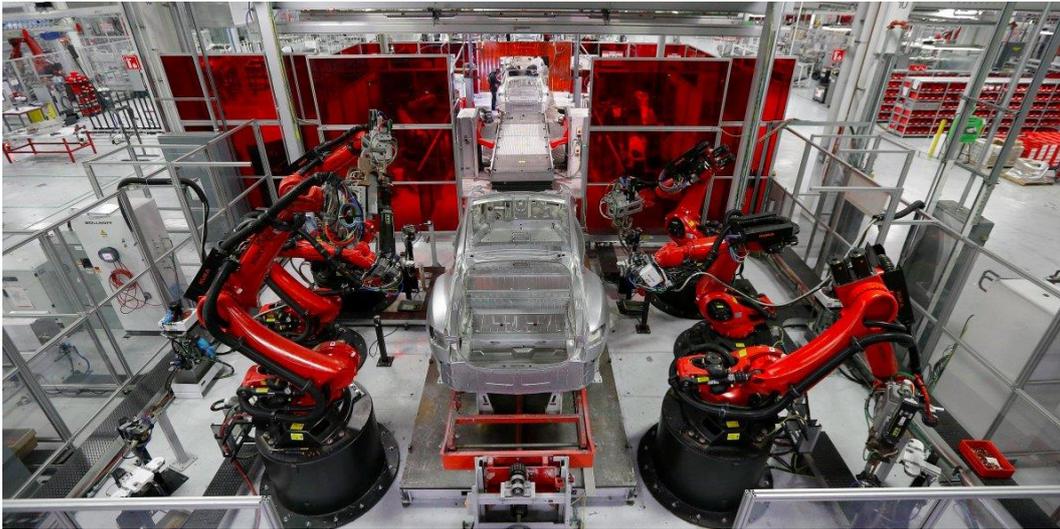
Assemblage et la peinture des carrosseries [11].
